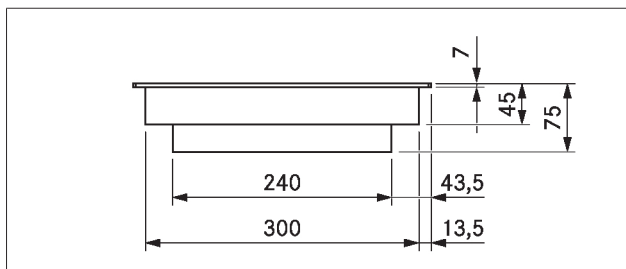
CKCB apparatets dimensjoner sett forfra
